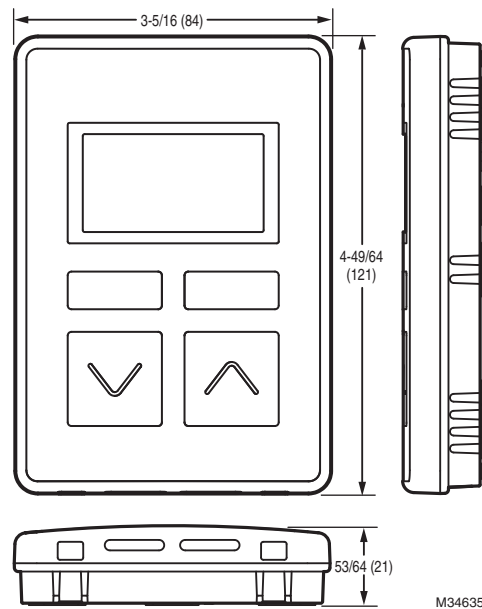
Dimensions du module mural ACL en pouces (mm).
